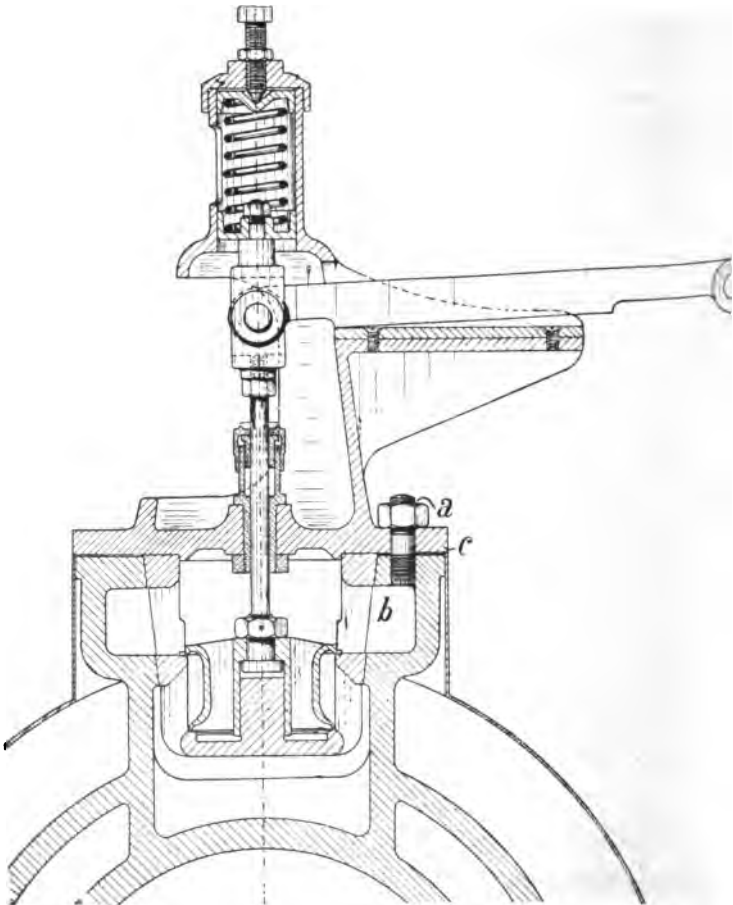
Einlassventil mit undichten Schrauben der Ventildeckel.
